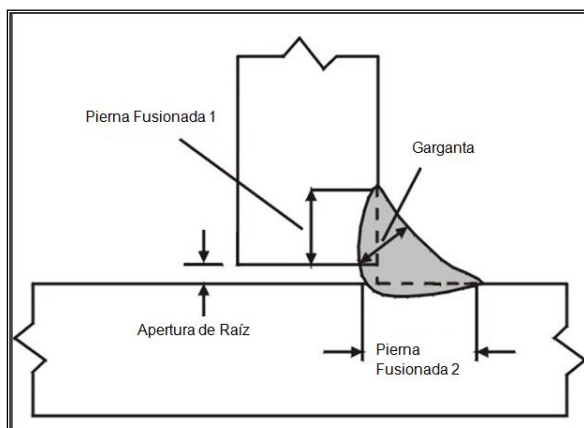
Unión en T con soldadura de filete y apertura de raíz^[1]
